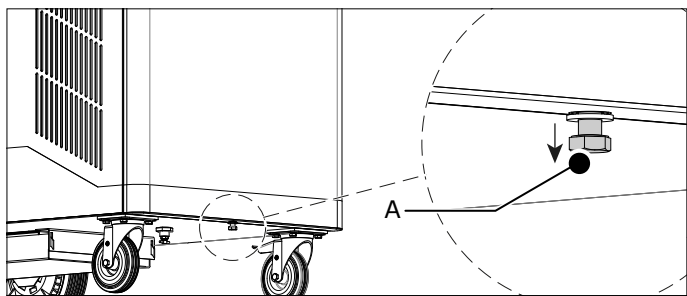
Schraube zum Entriegeln der Frontblende
